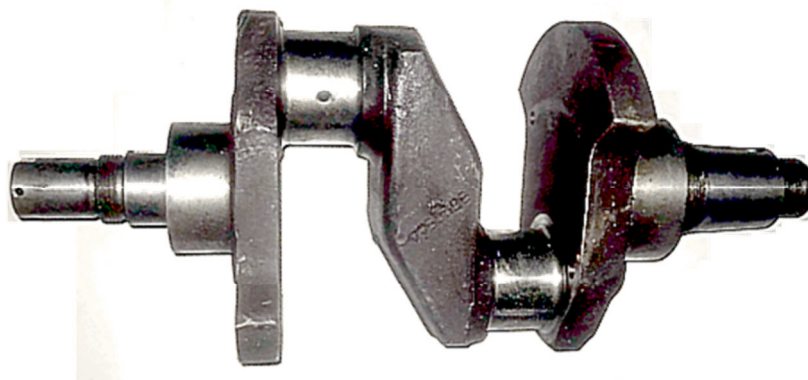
Неполноопорный коленчатый вал двигателя 2Ч8,5/11
